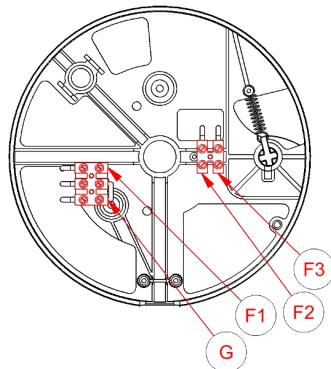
3 KABEL + Thermoschutzschalter
